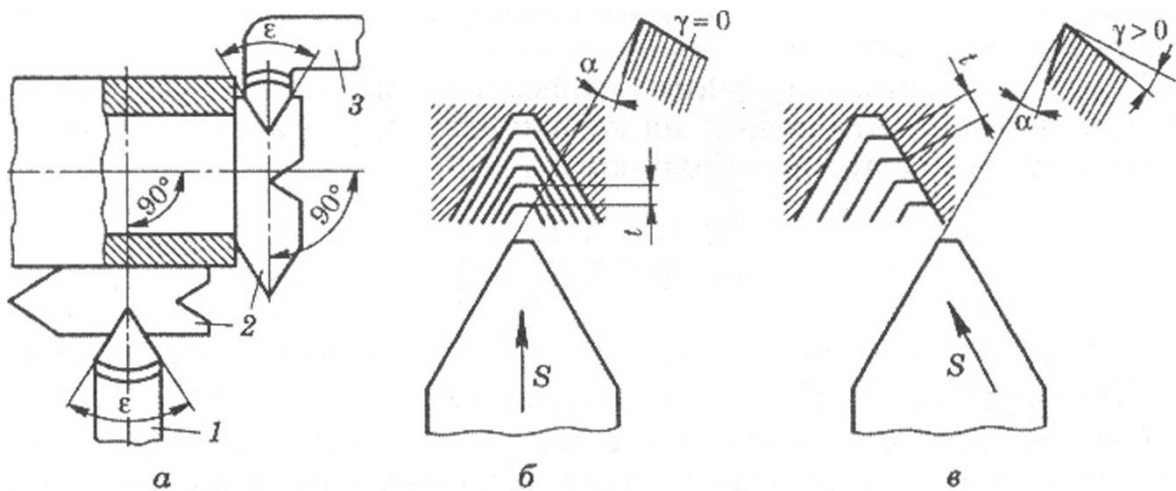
Схеми нарізування різьби різцями на токарному верстаті
